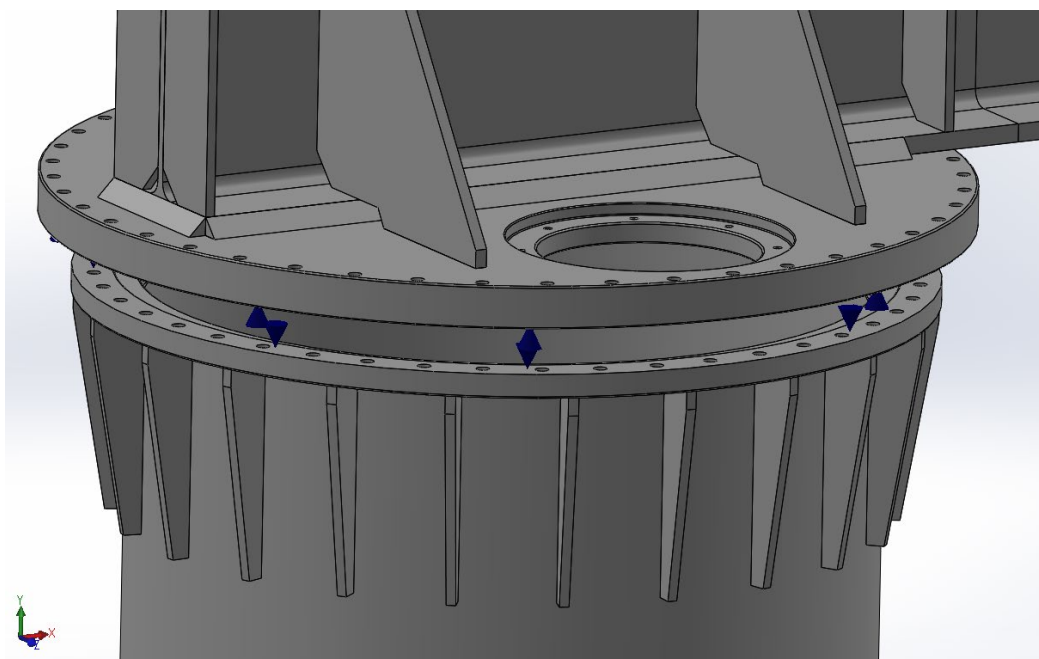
Detalle unión por conexión rígida entre conjunto superior a la columna.
